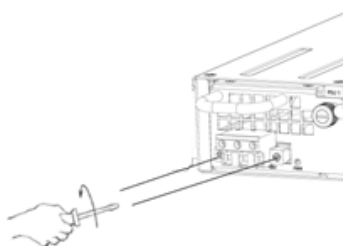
Removendo TERMINAL BLOCK da PSU 400/600 DC
